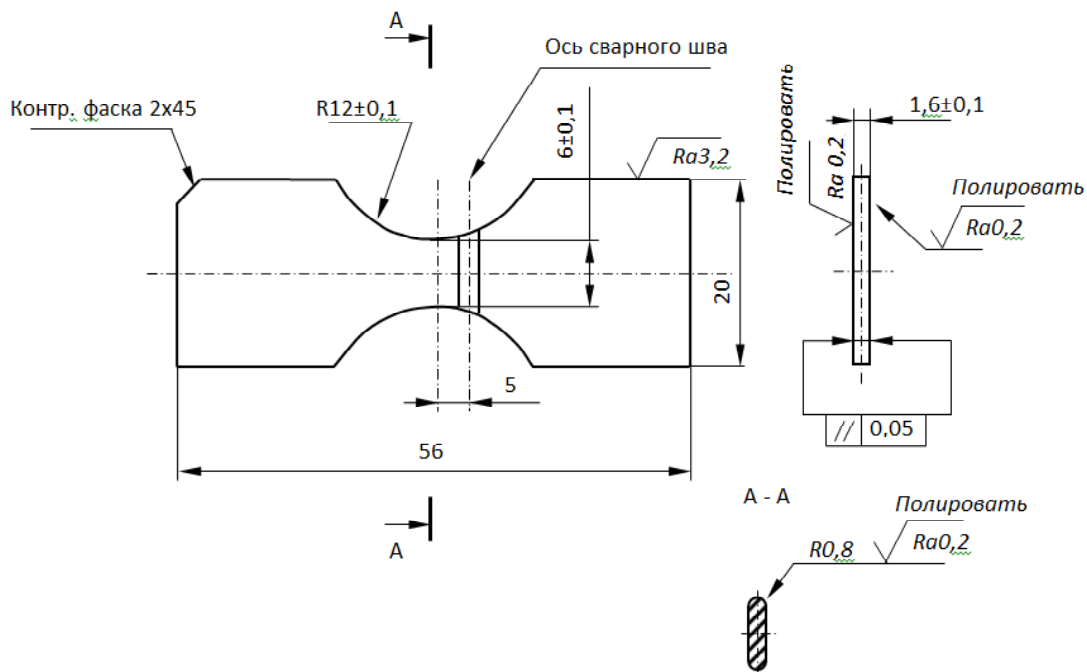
Эскиз сварного образца для испытаний на усталость
